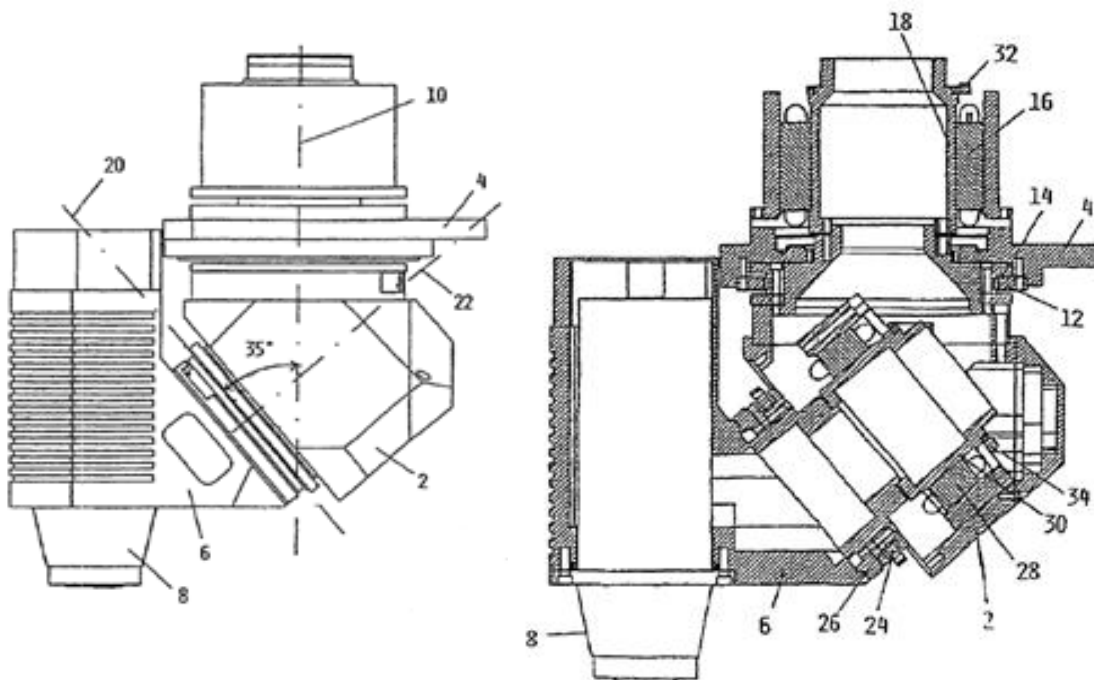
Aretace osy univerzální frézovací hlavy [22]      Obr. 37: Upínací šoupátko [22]
